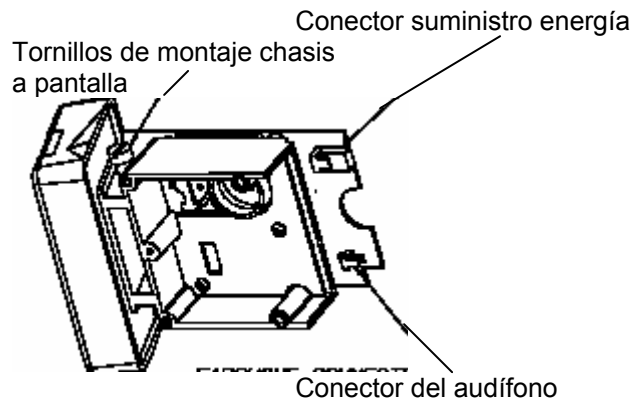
Localización de Tornillos de Montaje y Conector de Alimentación Eléctrica
